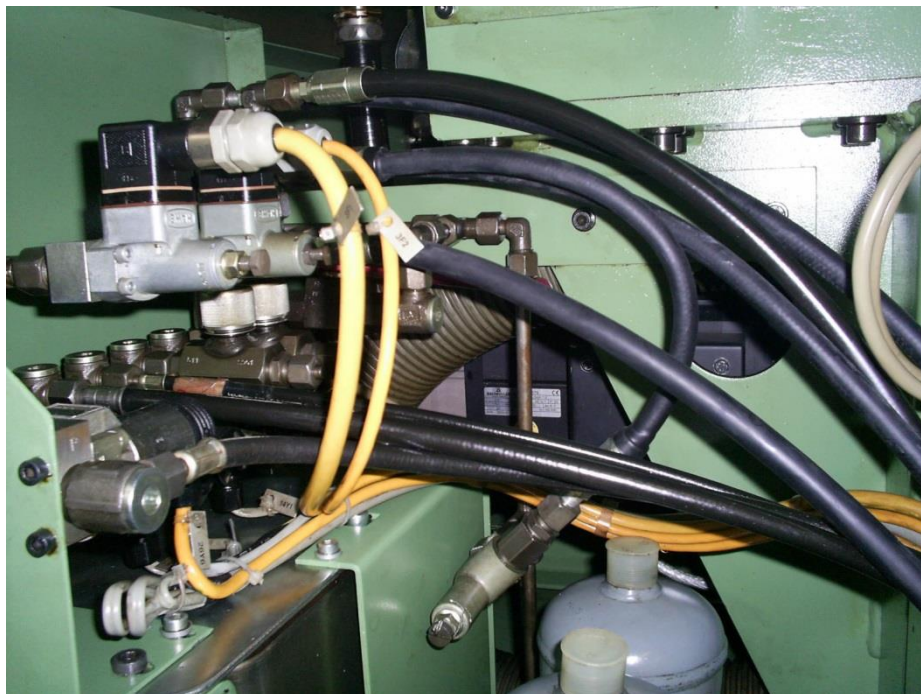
Общий вид гидроразветвителя трубогибочного станка
